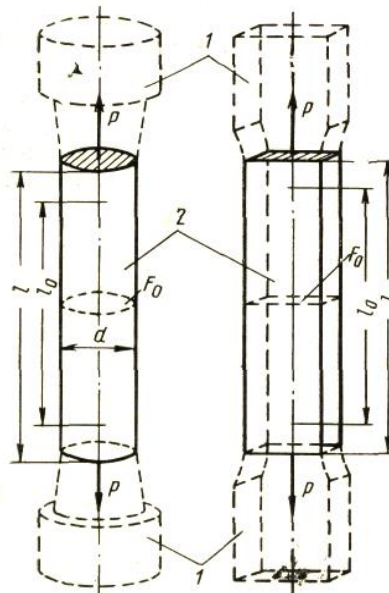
Зразки для випробування розтягування: 1– головки; 2 – робоча частина
